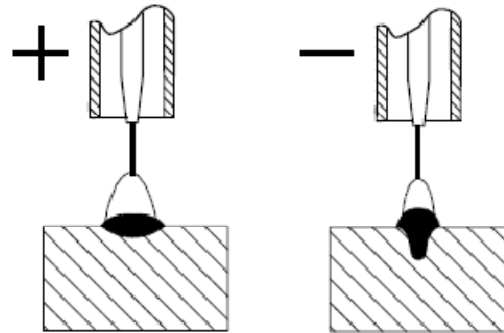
Efecto de la polaridad en el cordón de soldadura
